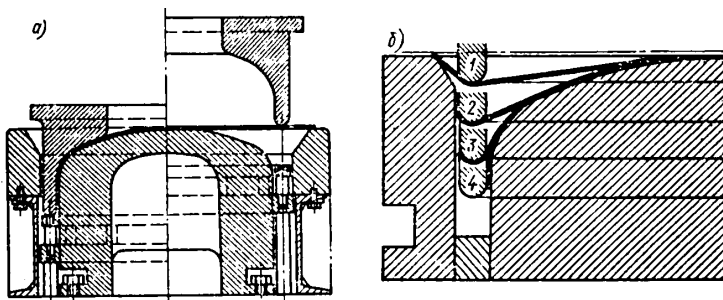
Витягування з подвійним перегином заготовки:
